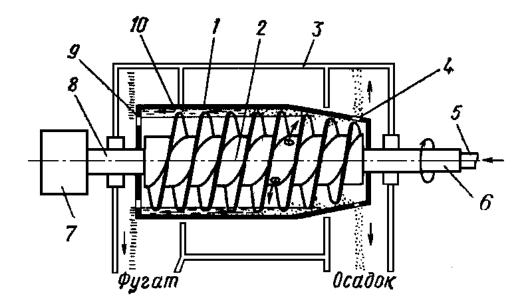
Принципиальная схема устройства центрифуги типа ОГШ: 1 — цилиндроконический ротор; 2 — шнек; 3— неподвижный кожух; 4 — разгрузочные окна для осадка; 5 — питающая труба; 5 — вал ротора; 7 — планетарный редуктор; 8 — вал шнека; 9 — сливные окна для фугата; 10 -жидкостный объем ротора.
